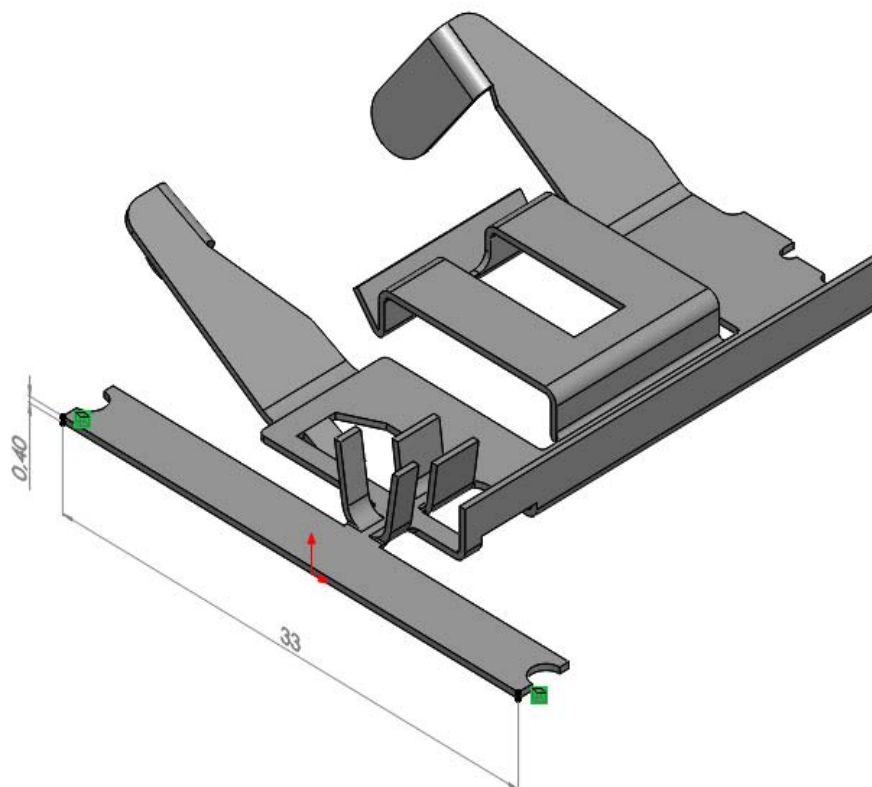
Detalhe da espessura do terminal e do passo entre furos para alimentação
